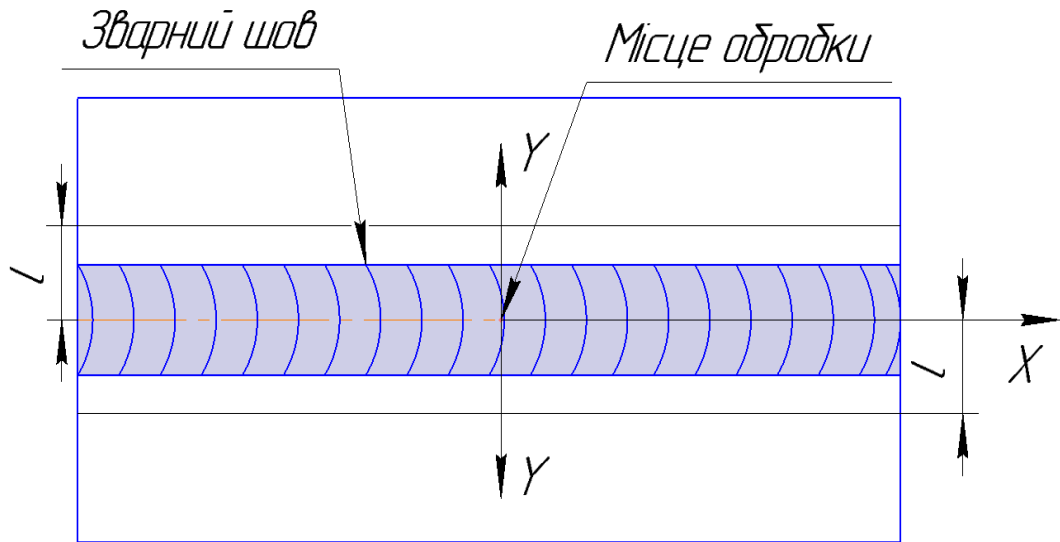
Схема ЕДО зварних пластин, де  $X$  та  $Y$  – координатні вісі,  $l$  – відстань від зварного з'єднання
